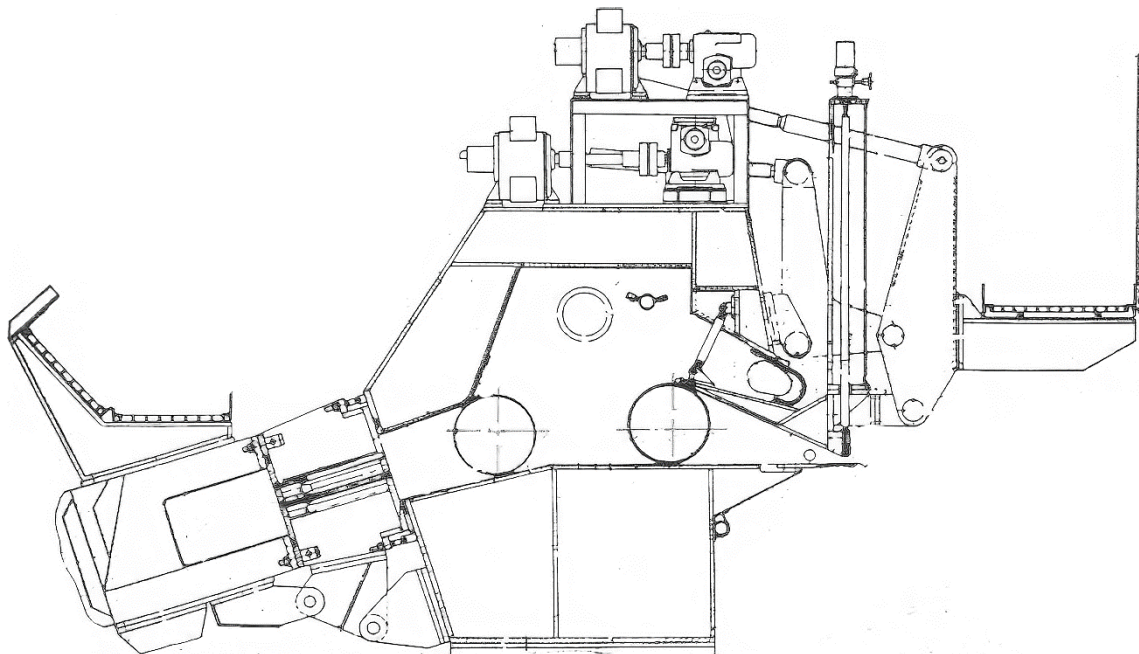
Напорный ящик закрытого типа с перфорированными валами последнего поколения для машин со скоростью до 900 м/мин (для машин К-33, К-34 ЦНИИБУММАШ)
